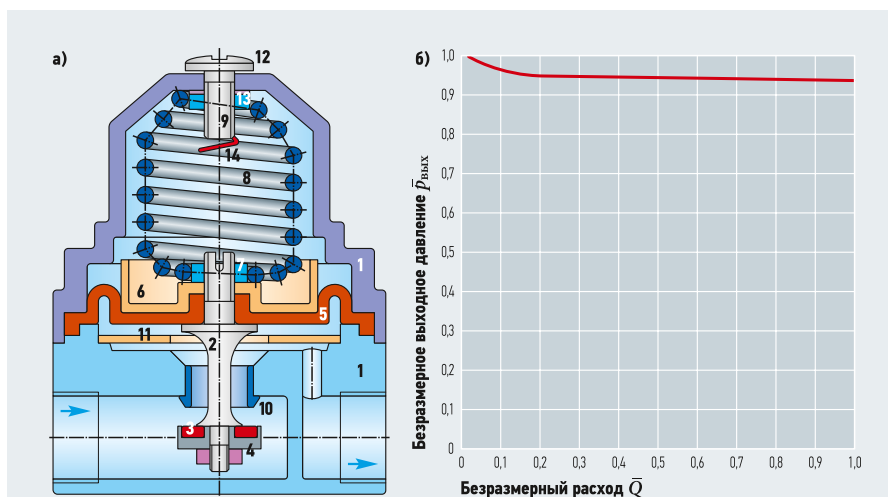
Принципиально-конструктивная схема (а) квартирного гидроредуктора (1 — корпус и крышка; 3 — уплотнительная прокладка; 4 — люлька; 5 — эластичная неармированная диафрагма; 6 — опорный диск; 7 и 13 — стальные гайки; 8 — пружина; 9 — корпус сапуна; 10 — седло; 11 — упорный диск; 12 — дренажное отверстие сапуна 9) и регулировочная характеристика настоящего квартирного редуктора воды (б)
